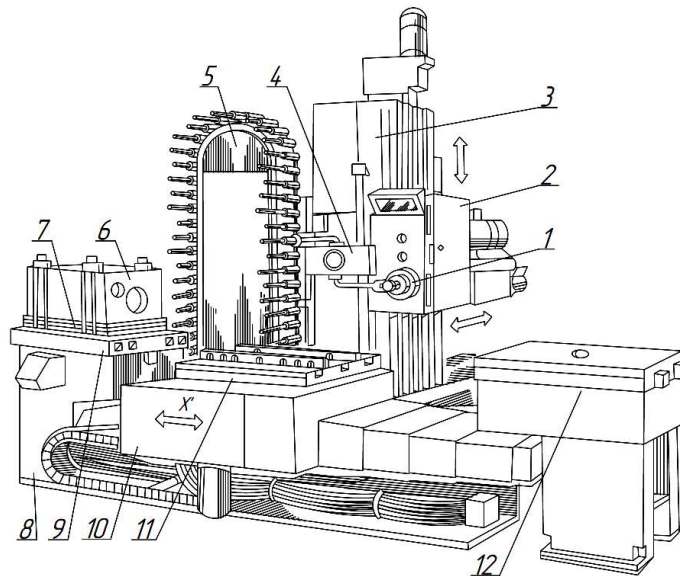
Загальний вигляд верстата 2623ПМФ4
